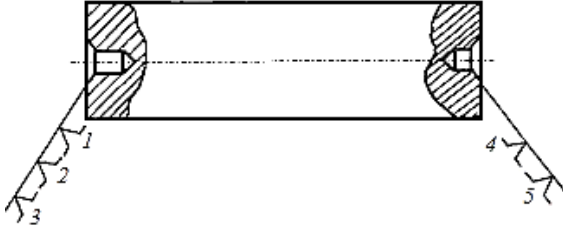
Схема базування вала по центровим отворах [2]
